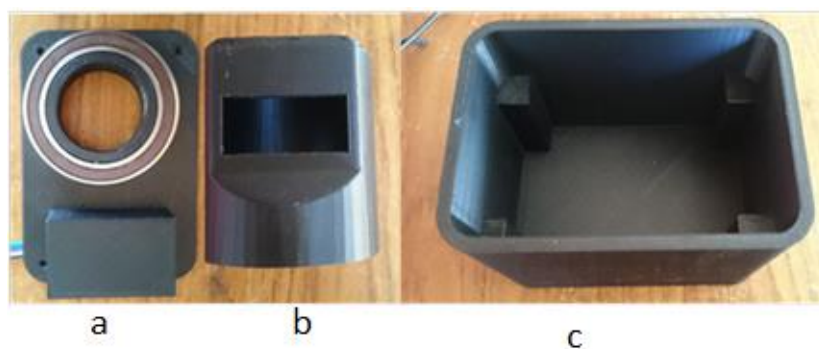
Componentes externos impresos; (a) tapa de la carcasa con rodamiento instalado, (b) cubierta del sensor y (c) carcasa.
